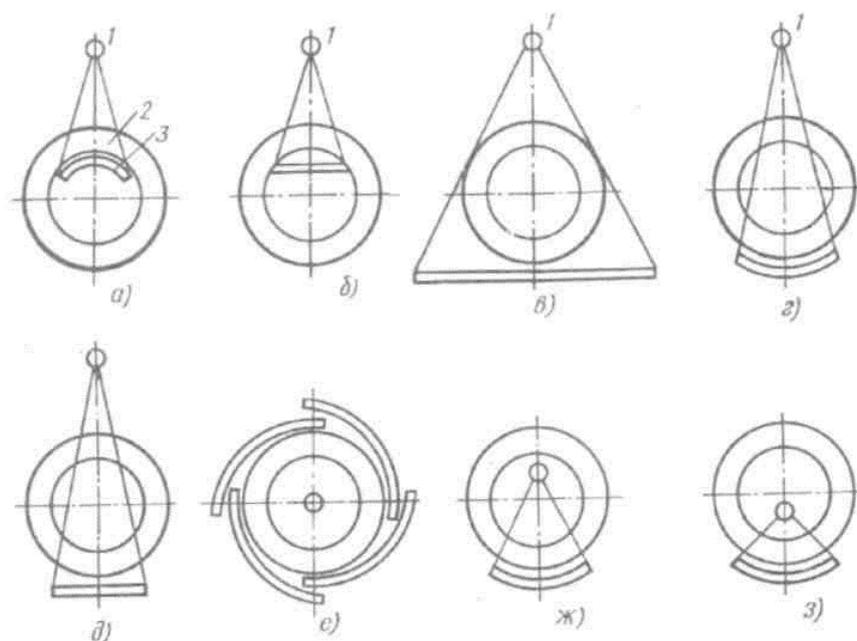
Схемы контроля кольцевых сварных соединений
